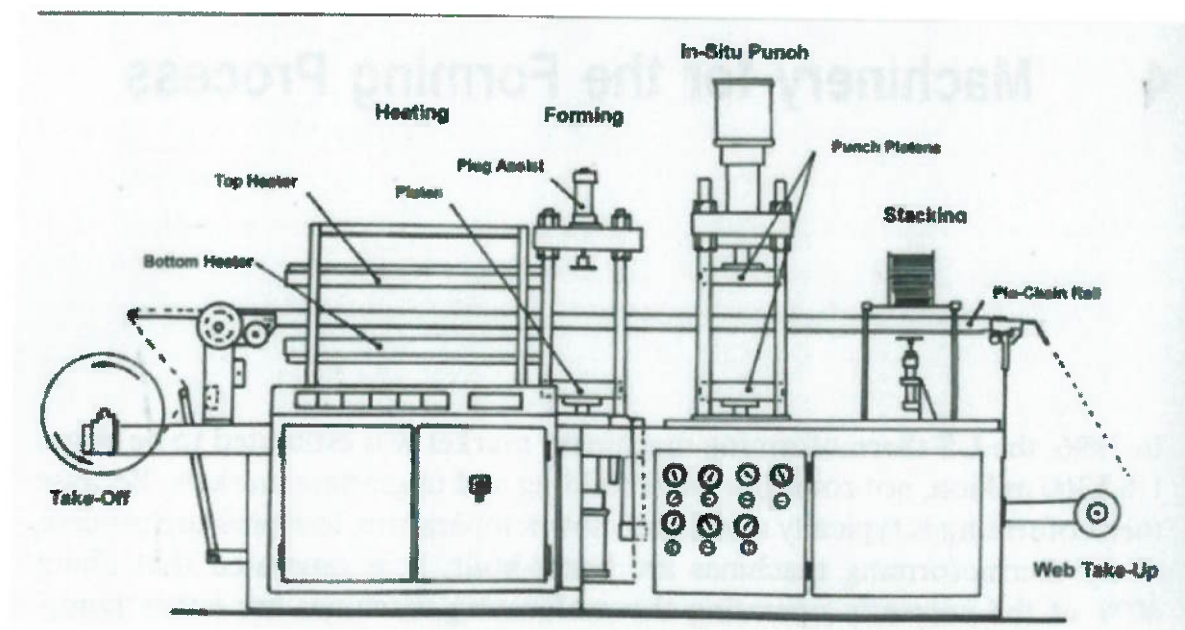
Desenho esquemático de uma máquina termoformadora do tipo roll fed Kiefel
